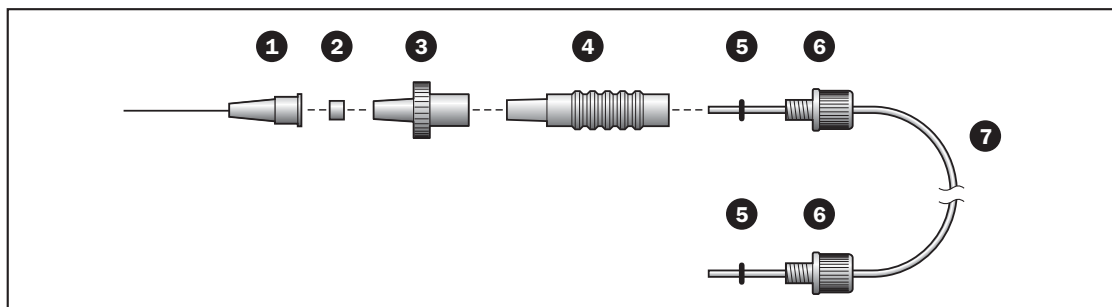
Vue d'ensemble de l'installation du TGC-2.
